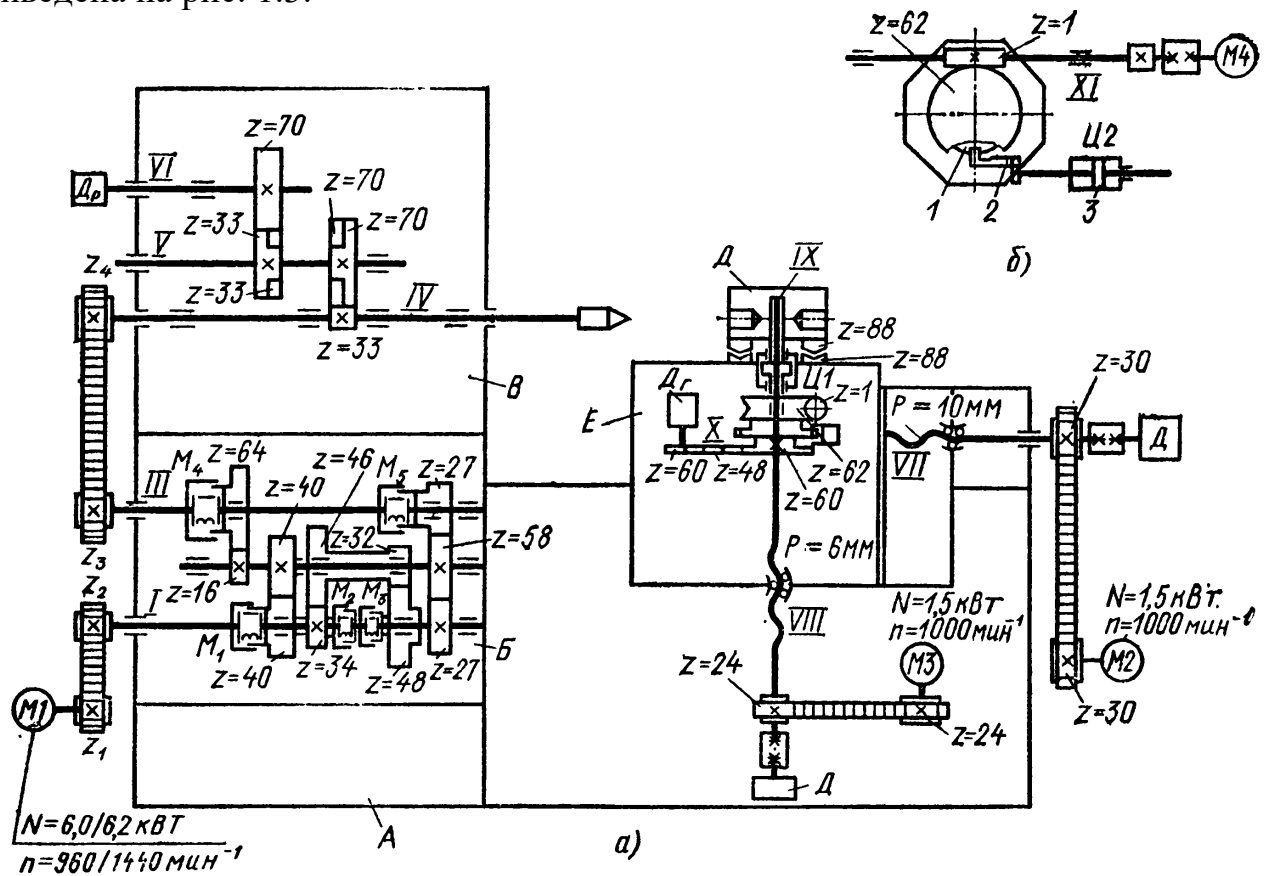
Кінематична схема токарно-револьверного верстату з ЧПК мод. 1В340Ф30
